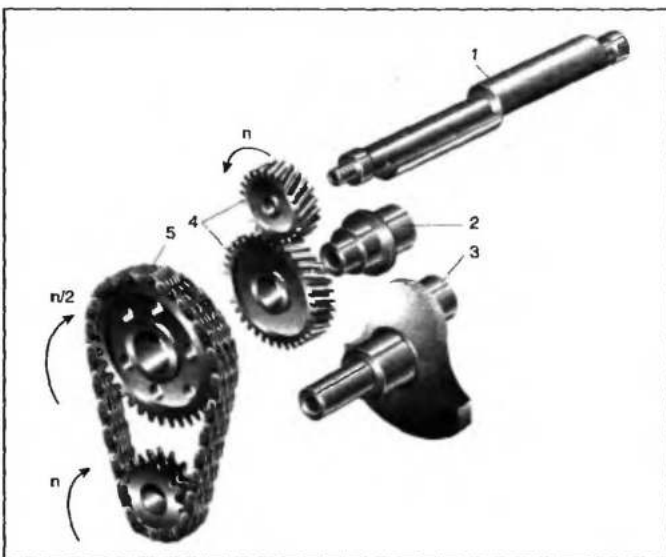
Балансирующий вал V-образного 6-цилиндрового двигателя с нижним расположением распределительного вала: 1 — балансирующий вал; 2 — распределительный вал; 3 — коленчатый вал; 4 — пара шестерен; 5 — цепная передача
